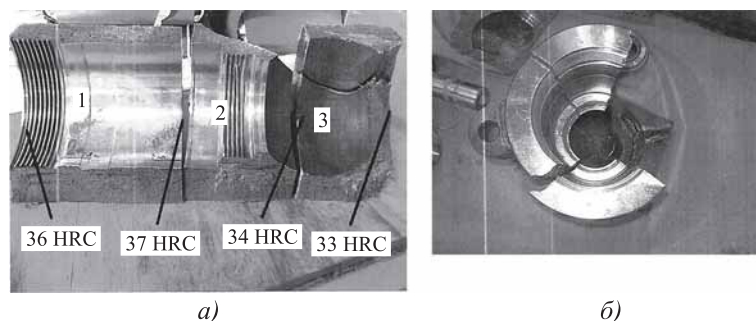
Разрушенный при приемосдаточных испытаниях корпус поглощающего аппарата, изготовленного из стали 30ХГСН2А: а — разделенный на фрагменты корпус; б — донная часть корпуса
